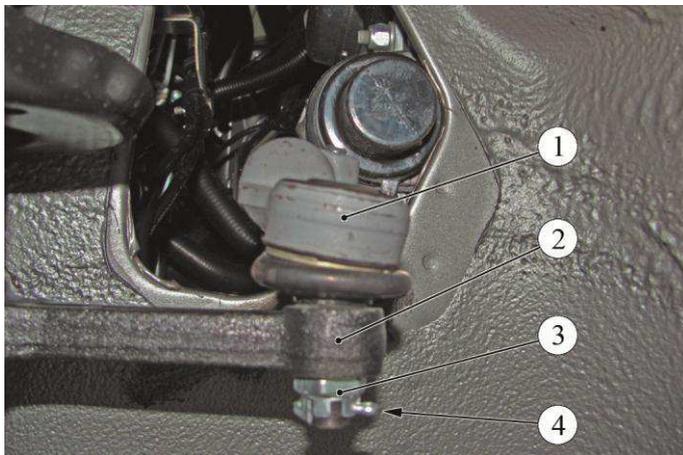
Выпрессовка шарового пальца наконечника рулевой тяги:
